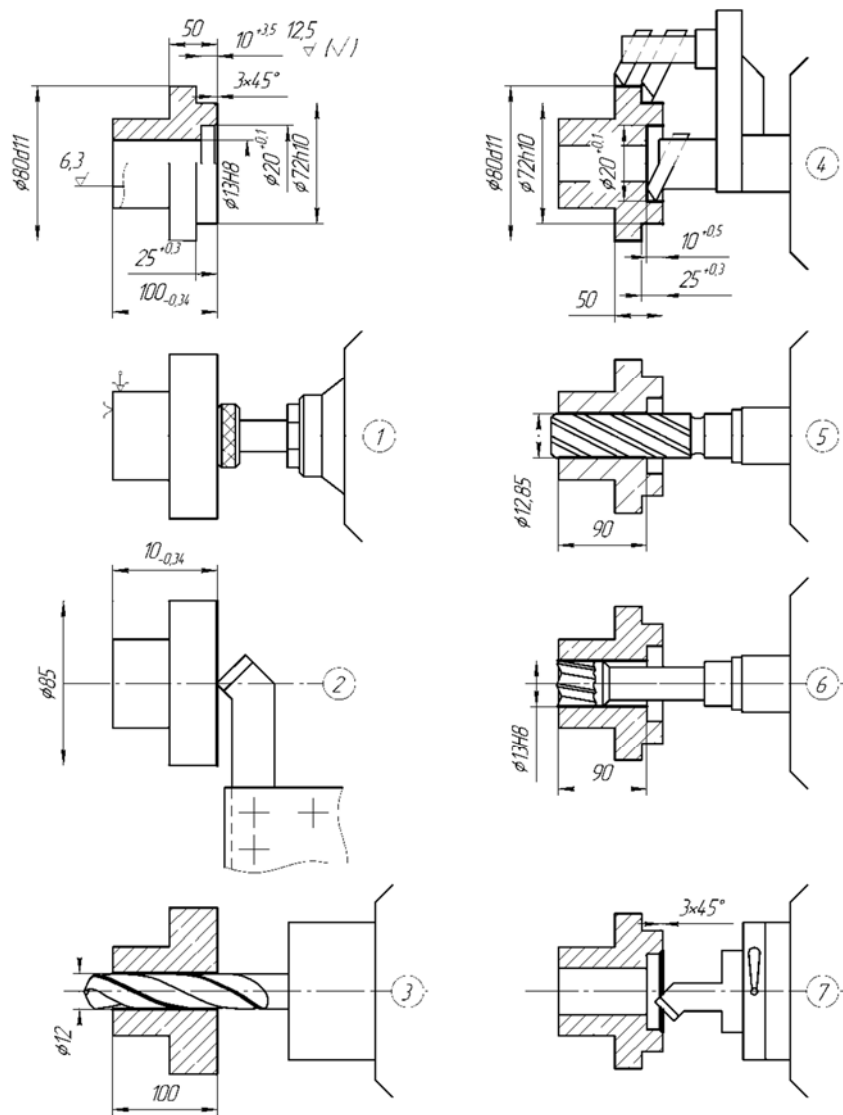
Пример наладки токарно-револьверного станка с вертикальной осью револьверной головки
